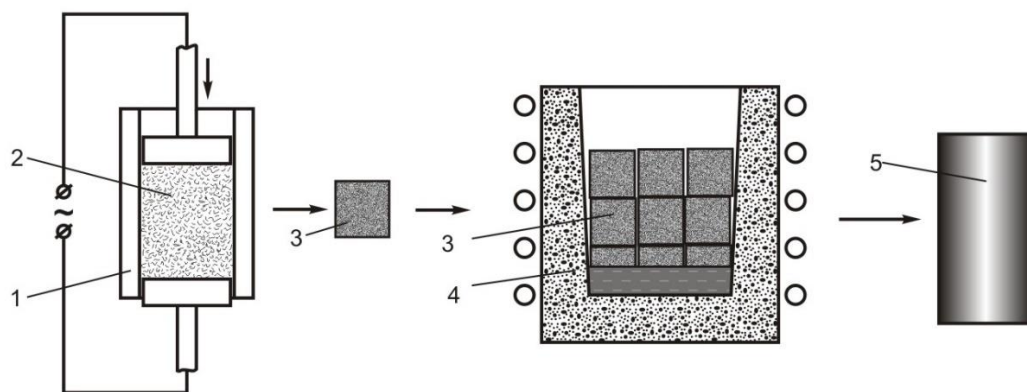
Схема переробки пресованої стружки в індукційній печі:
